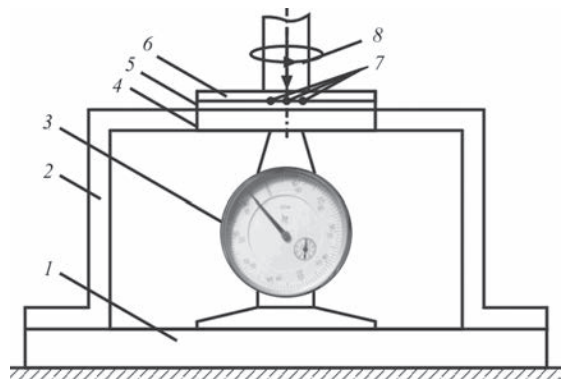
Схема стенду для досліджень: 1 — опорна плита верстату; 2 — каркас стенду; 3 — динамометр; 4 — рухома плита; 5 — теплоізолятор; 6 — зварюваний зразок; 7 — термопари; 8 — робочий інструмент
